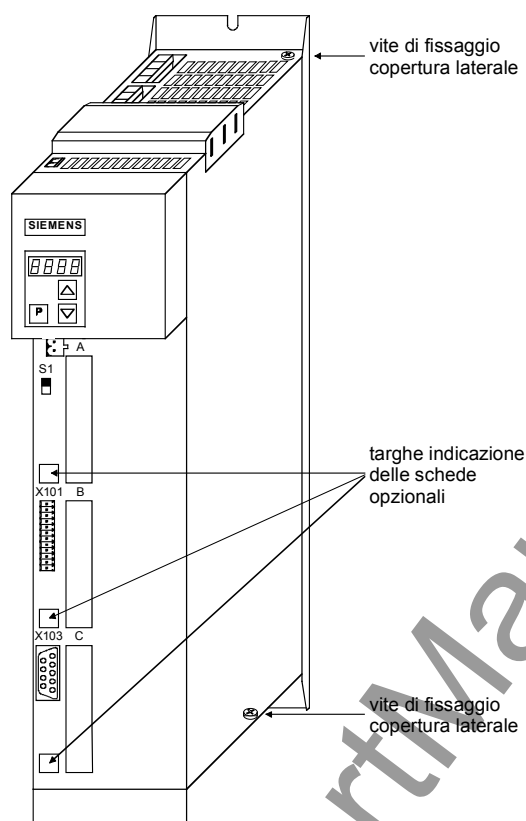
Posizione delle viti di fissaggio della parete laterale destra
